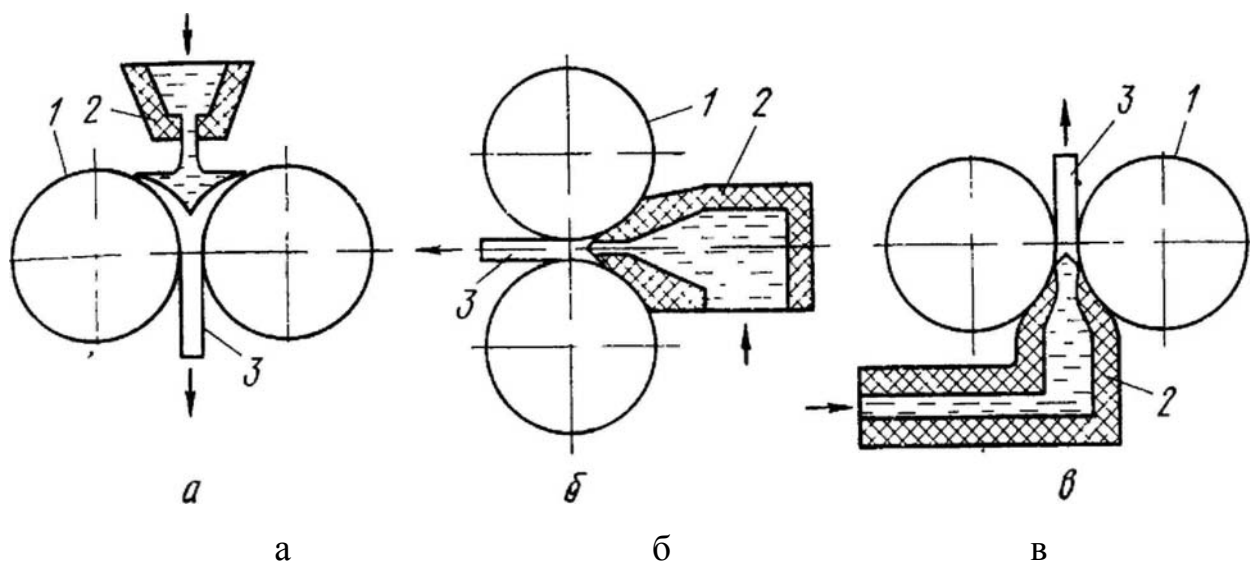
Валковые кристаллизаторы с заливкой расплава: а – сверху; б – сбоку; в – снизу: 1 – валки-кристаллизаторы; 2 – заливочное устройство; 3 – сформированная заготовка
